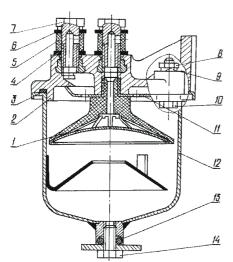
Фильтр грубой очистки топлива 1-отражатель с сеткой; 2- корпус; 3- кольцо; 4, 6, 13- кольцо уплотнительное; 5- втулка защитная; 7- болт поворотного угольника; 8- гайка; 9-шайба; 10- болт; 11- рассеиватель; 12- стакан; 14- пробка
